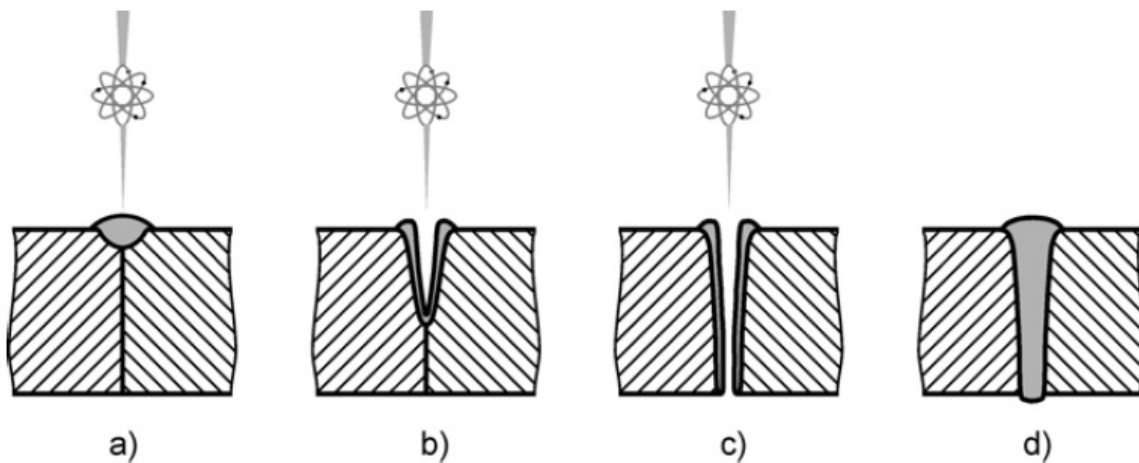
Aufschnelzen der Schweißfuge [5]
